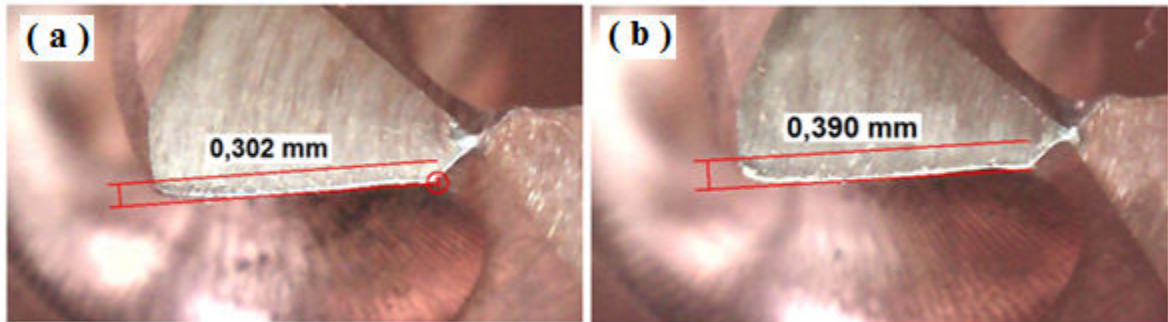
Desgaste de flanco das brocas não revestidas desgastadas: (a) comprimento usinado de 3072 mm, (b) comprimento usinado de 4608 mm
